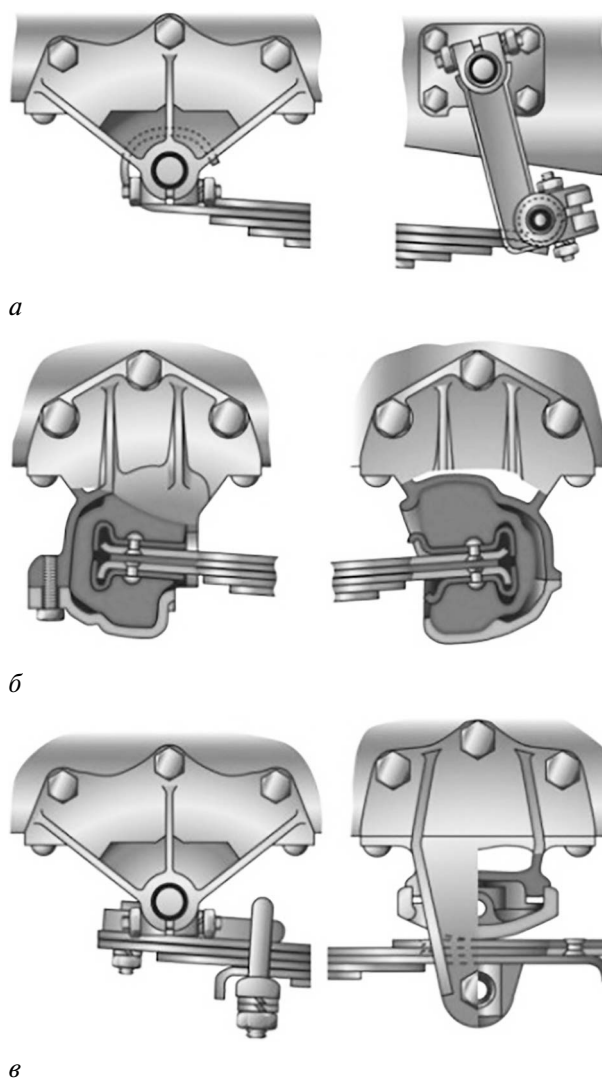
Крепление передних рессор [12]: а — с витыми ушками; б — на резиновых подушках; в — с накладным ушком и скользящей опорой
